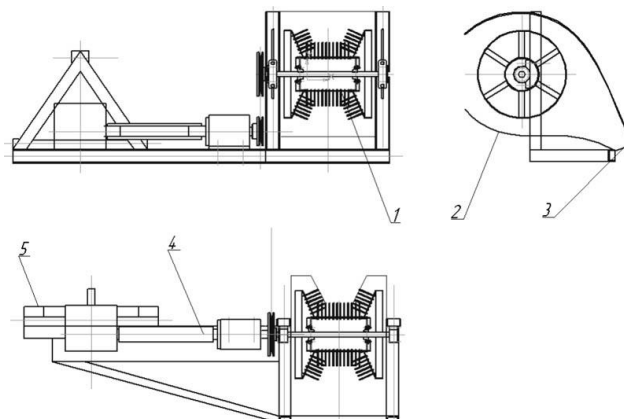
Однобарабанный очісуючий пристрій: 1 - очісуючий барабан, 2 – кожух, 3 – прийомна камера, 4 - механізм приводу, 5 – навісний механізм.
